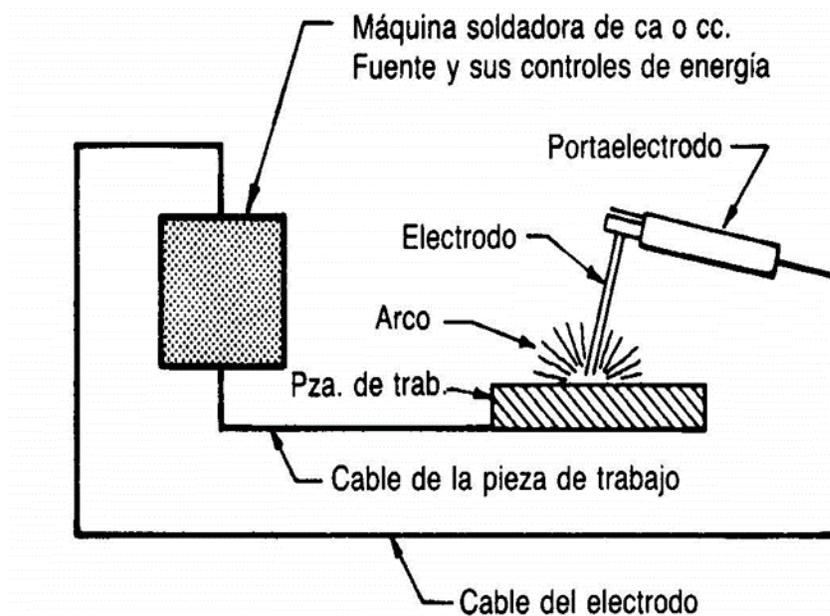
soldadura por arco manual con electrodo revestido
